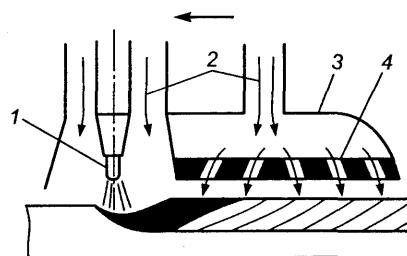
Сварка титана с подачей защитного газа в горелку с насадкой:
